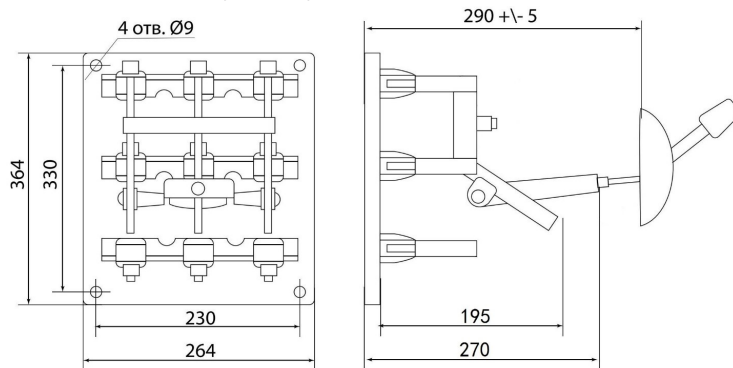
Разъединитель серии Р с боковой рукояткой РБ-6, на номинальный ток 630 А
